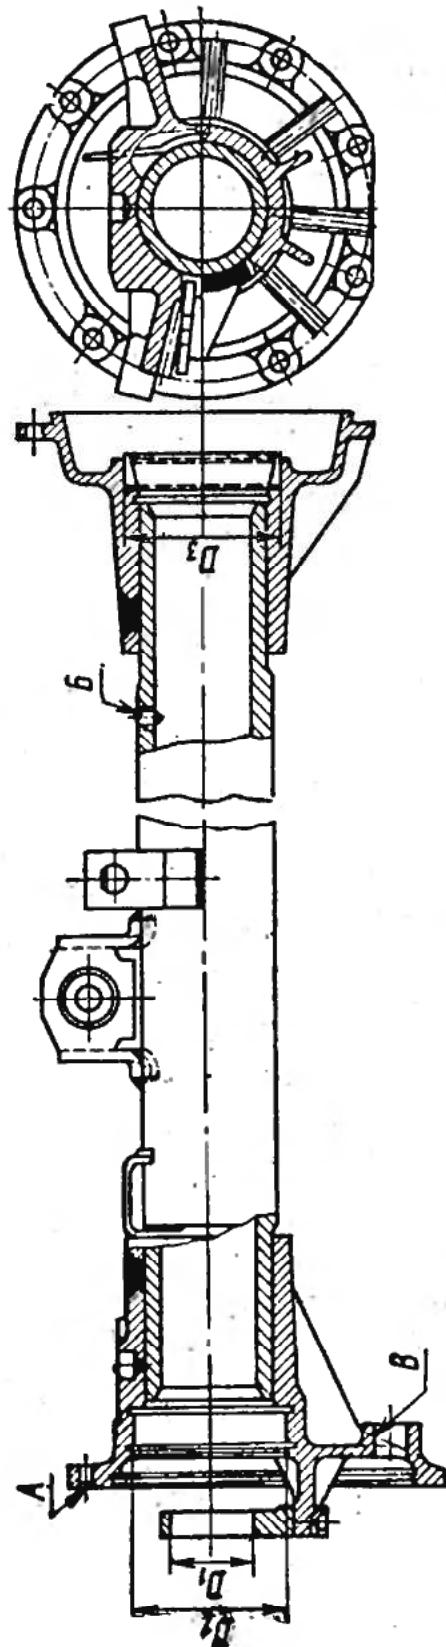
Крышка картера заднего моста с кожухом полуоси и картером колесного редуктора в сборе
